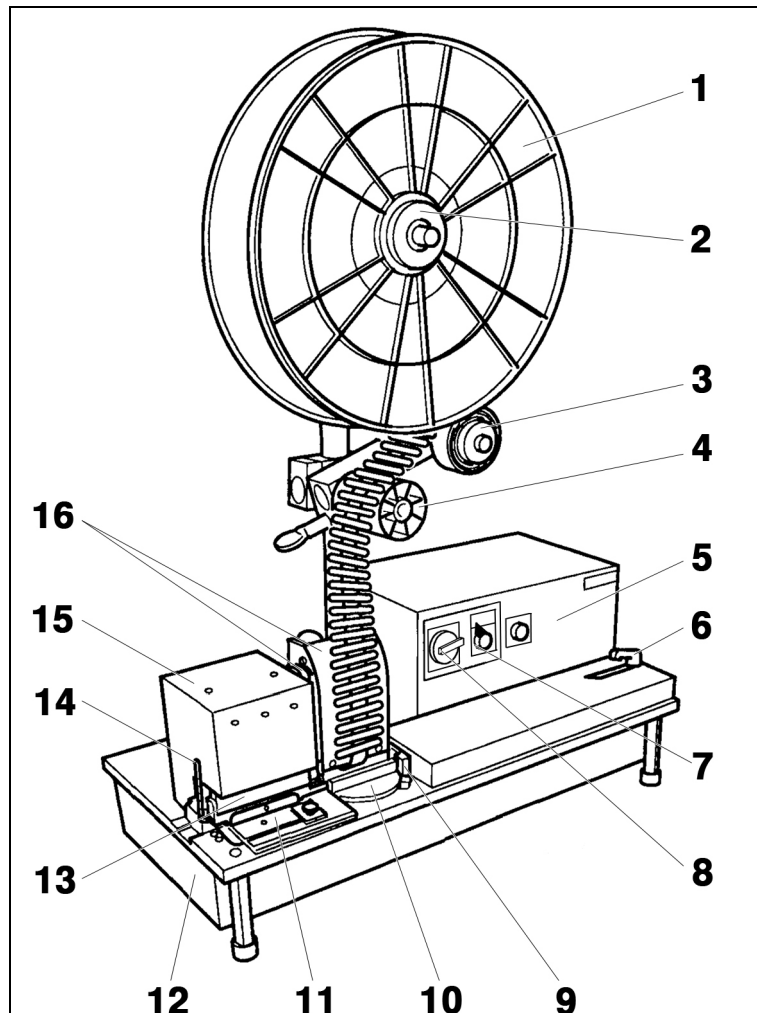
Gesamtansicht (Ausführung LATCH Maschine)
